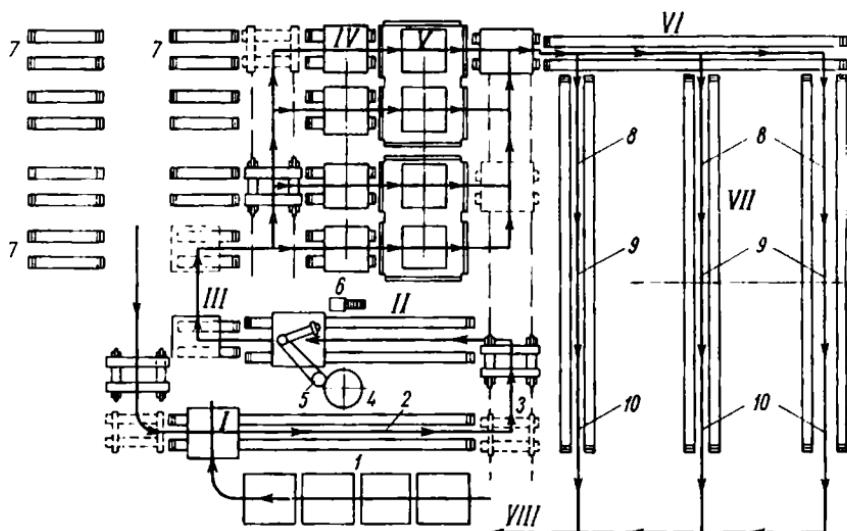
Схема рольганговой линии «скользящей оснастки» с пескометом для крупных форм:
